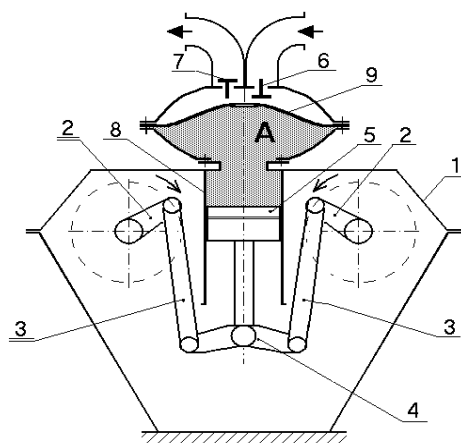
Полуконструктивная схема бесползунного мембранно-поршневого насоса, где: 1 – корпус насоса, 2 – кривошипные валы, 3 – шатуны, 4 - коромысло, 5 – поршень, 6 и 7 - всасывающий и нагнетательный клапаны, 8 – цилиндр насоса, 9 - мембрана.
